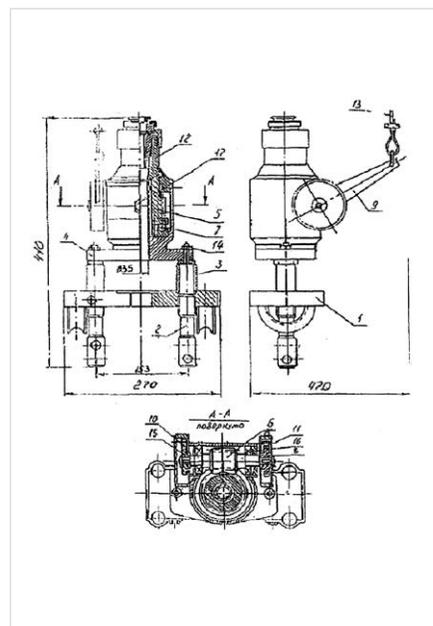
Штанговращатель ШВЛ—10В: 1 — траверса нижняя; 2 — винт грузовой; 3 — втулка распорная; 4 — корпус; 5 — колесо червячное; 6 — червяк; 7, 16 — подшипник; 8, 15 — храповик; 9 — рычаг; 10, 11 — собачка; 12 — блок сухарей; 13 — канат; 14 — гайка; 17 — пробка
